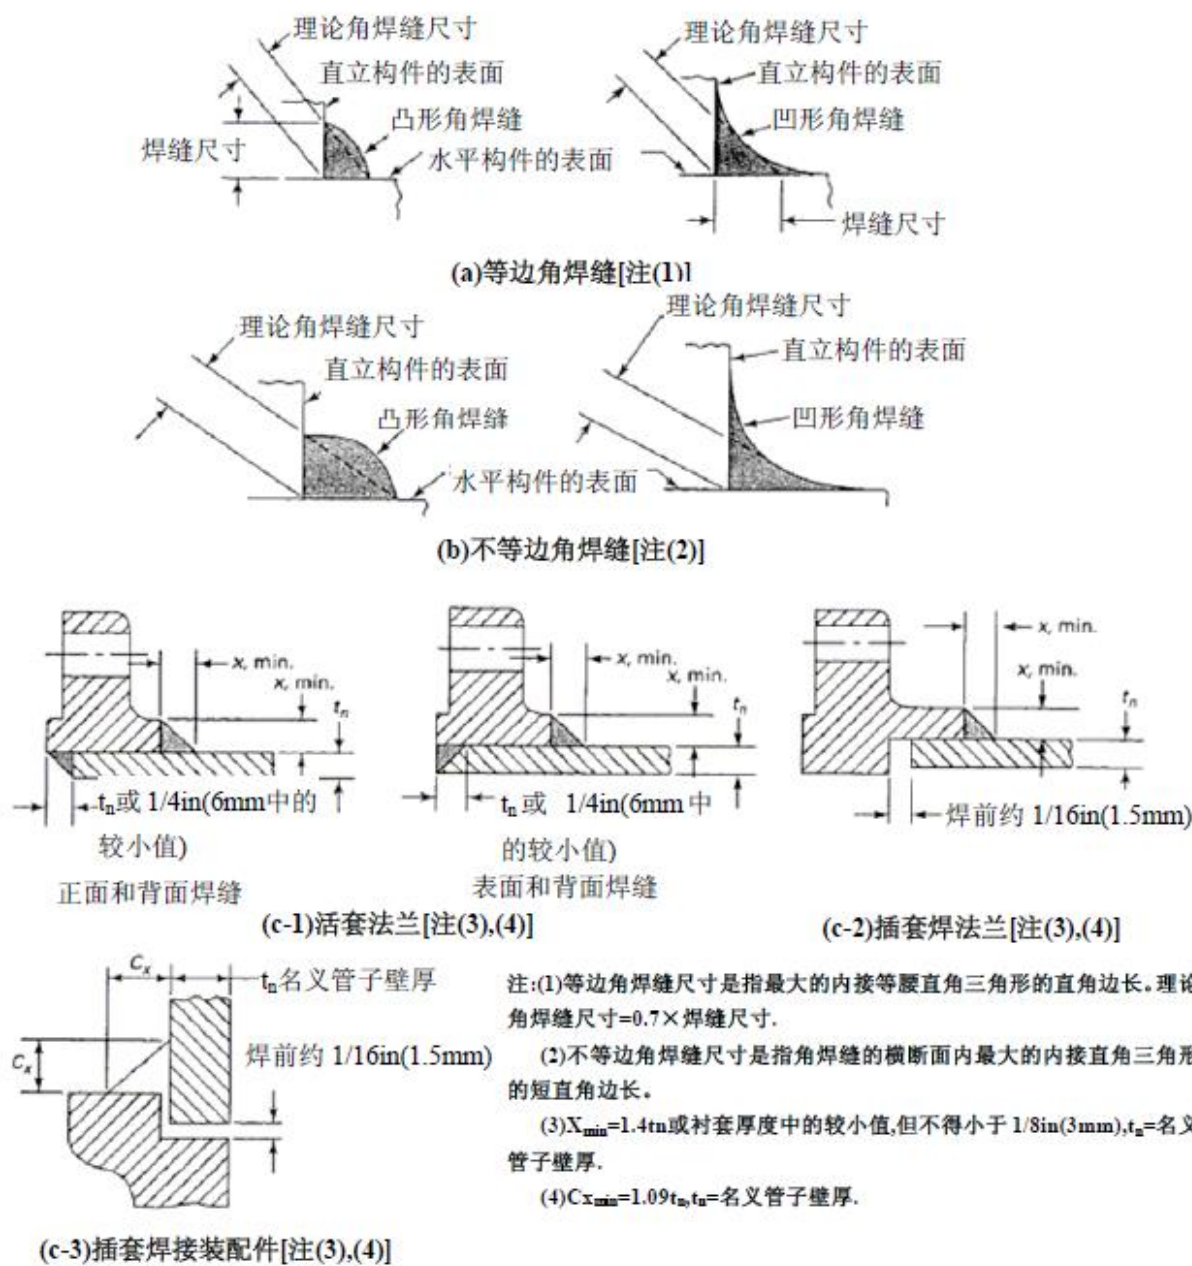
角焊缝、插套焊缝的尺寸和详图
